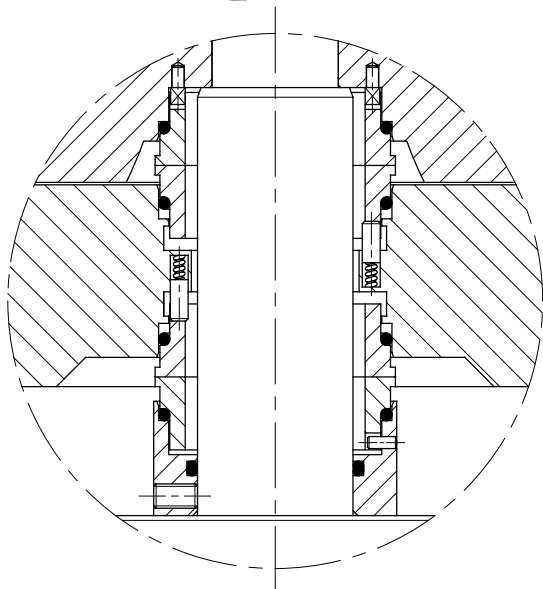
Детальный вид для размера ME-6125/6130 RE.
